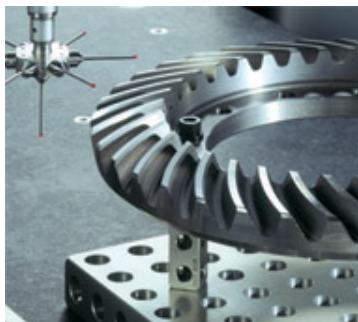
Maquina inspección de engranajes medición por coordenadas (fuente frencio)
